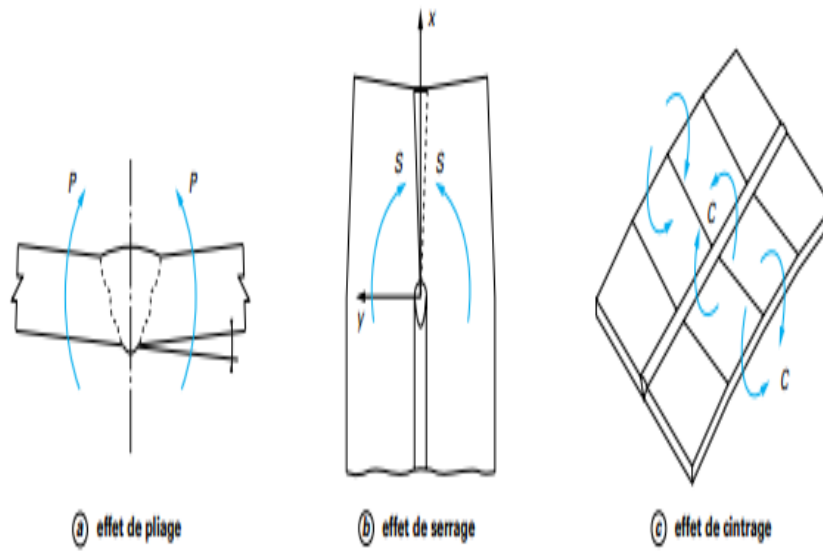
Les trois composantes de rotation observables sur un assemblage bout à bout rectiligne multi passe
